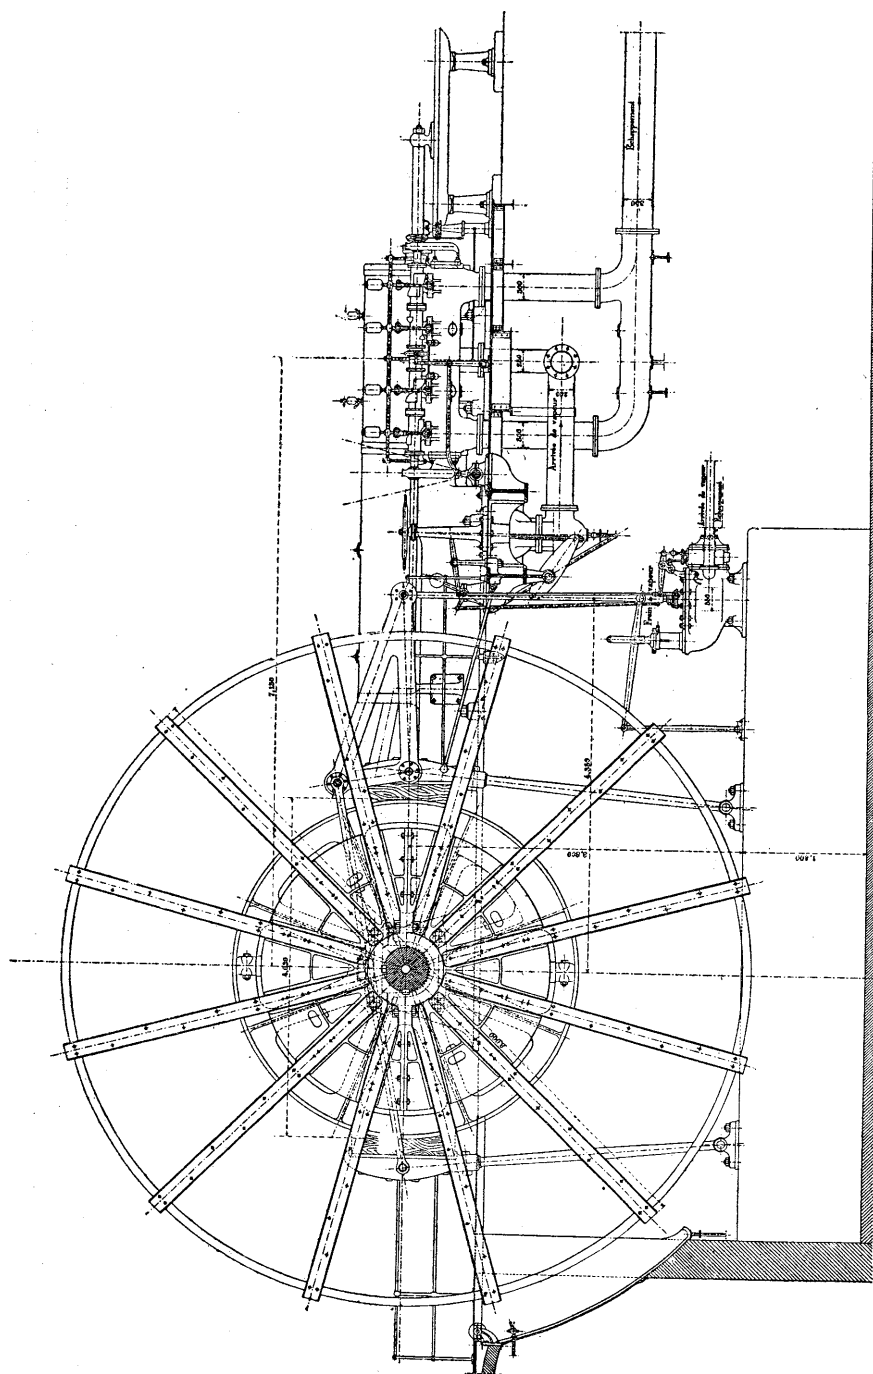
Machine d'extraction de Bruay. — Coupo longitudinal.
